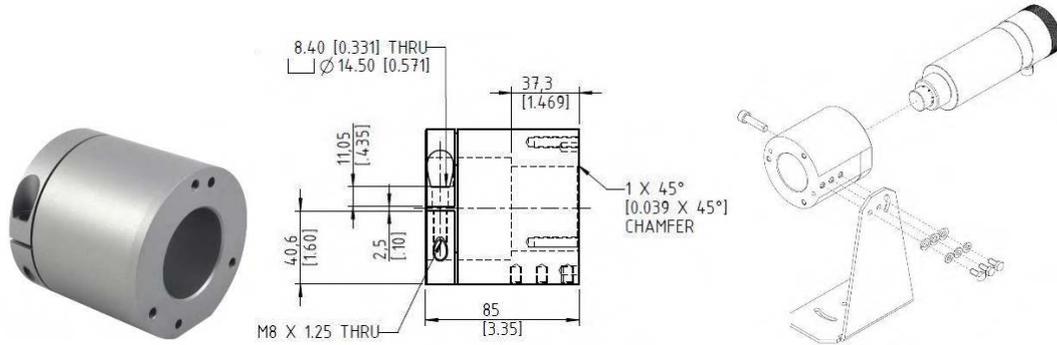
Vue et dimensions de l'adaptateur (E-UAA)
